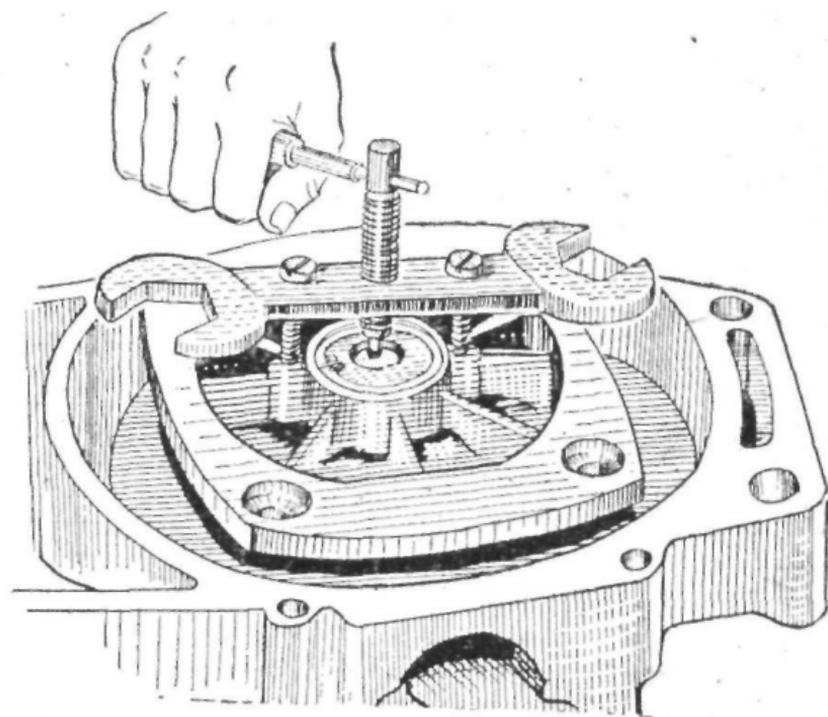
Снятие крышки кривошипной камеры двигателя ИЖ-Ю.
